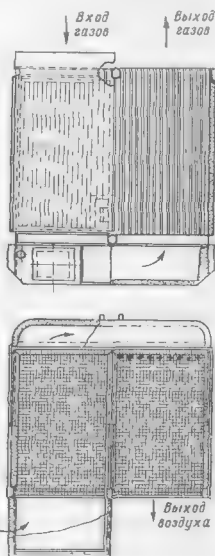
Трубчатый воздухоподогреватель котла ДКВр-10-39
